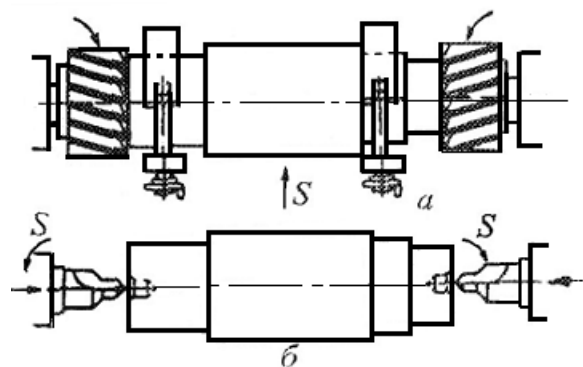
Схеми обробки торців валів на фрезерно-центрувальних верстатах
